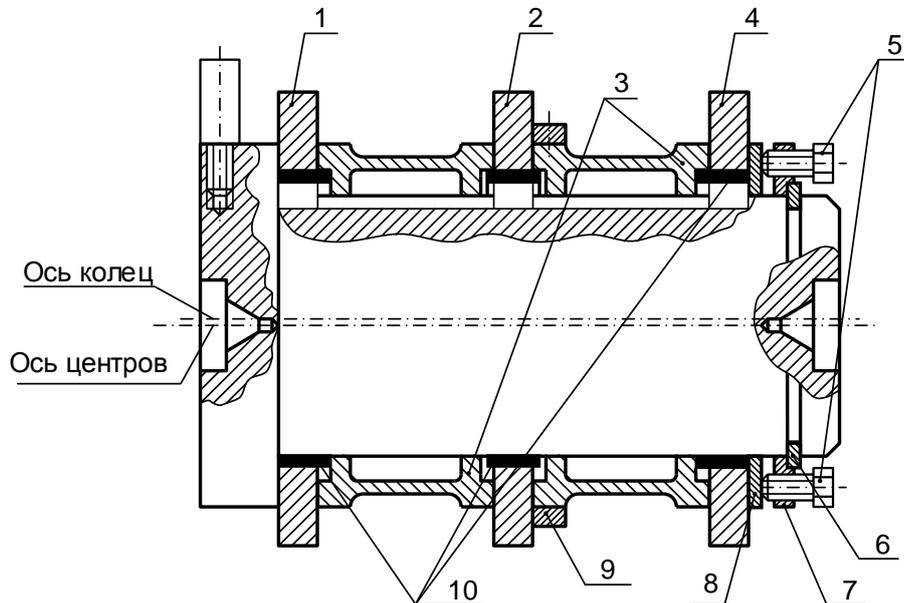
Оправка с кольцами-заготовками: 1, 2 и 4 – обрабатываемые сменные кольца; 3 – распорные втулки; 5 – стяжные болты; 6 – размерное кольцо; 7 – упругое кольцо; 8 – упорное кольцо; 9 – градуированное кольцо для фиксации углового положения оправки; 10 – эксцентрические кольца
